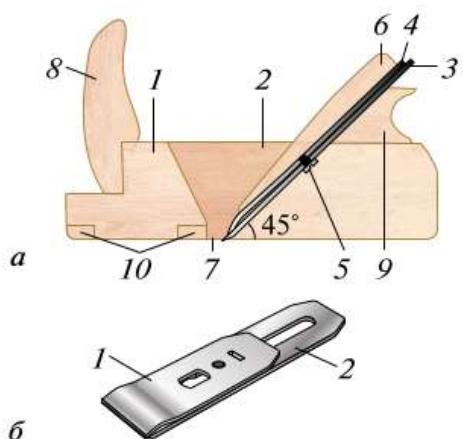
Рубанок с двойной железкой: а — общий вид;
